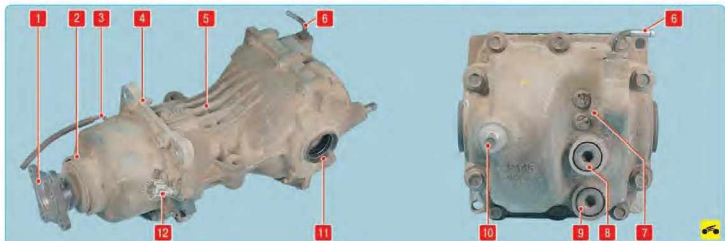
Редуктор заднего моста: 1 – фланец редуктора заднего моста; 2 – корпус электромагнитной муфты; 3 – корпус электромагнитной муфты; 4 – фланец переднего кронштейна подвески редуктора; 5 – картер редуктора заднего моста; 6 – сапун редуктора заднего моста; 7 – крышка картера редуктора заднего моста; 8 – пробка контрольного (наливного) отверстия редуктора заднего моста; 9 – пробка сливного отверстия редуктора заднего моста; 10 – задний кронштейн подвески редуктора; 11 – сальник привода заднего колеса; 12 – колодка проводов электромагнита муфты
